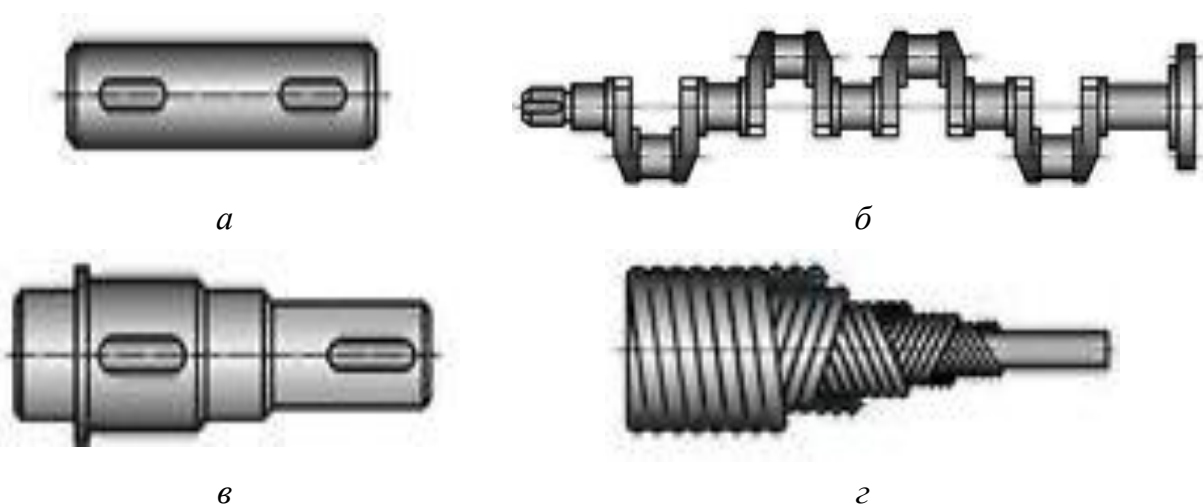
Конструкции валов: *а* — гладкий; *б* — коленчатый; *в* — прямой вал переменного сечения (ступенчатый); *г* — гибкий вал
